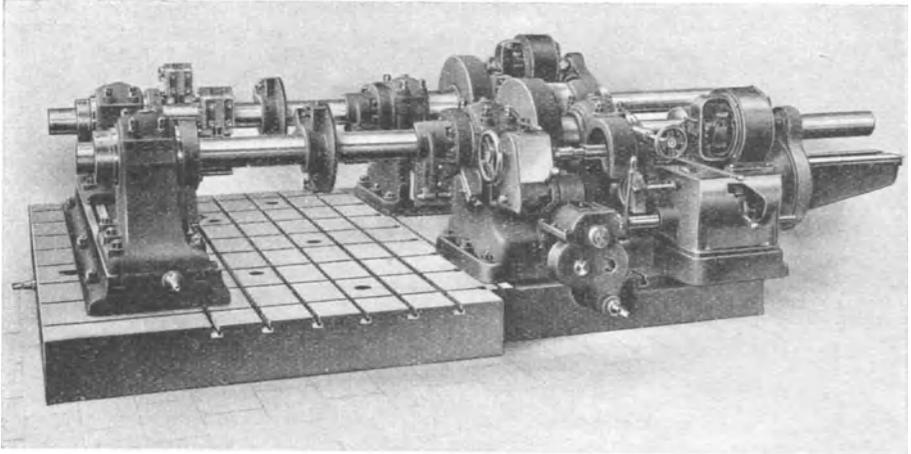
Maschine mit verschiebbarer Bohrstange.
